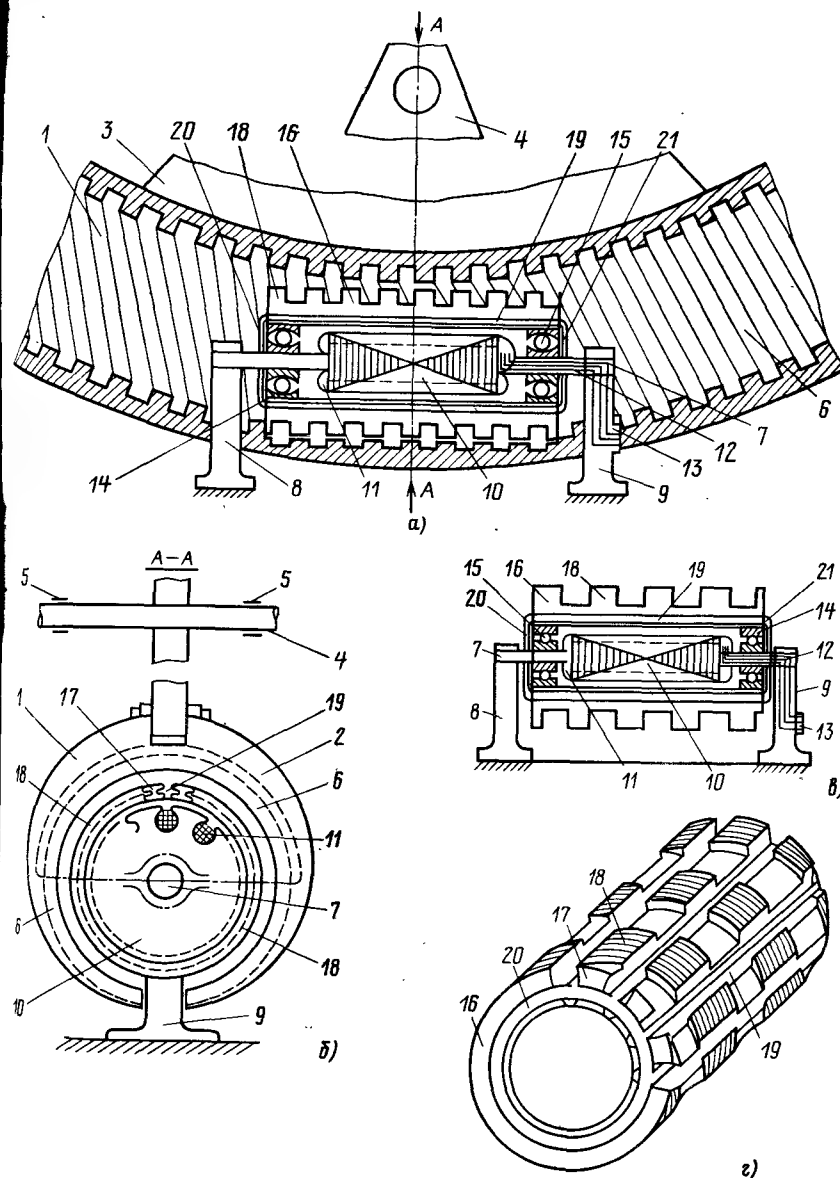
МДД с ротором в виде полого цилиндра:
